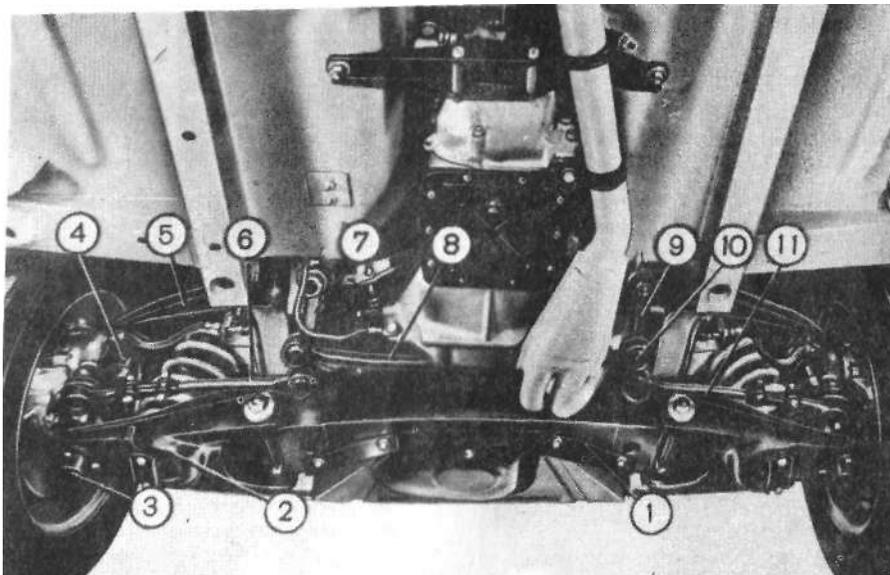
Передняя подвеска и рулевое управление: 1 — поперечина; 2 — нижний рычаг; 3 — шаровая опора нижнего рычага; 4 — шаровая опора верхнего рычага; 5 — верхний рычаг; 6 — боковая рулевая тяга левая; 7 — сошка; 8 — средняя рулевая тяга; 9 — маятниковый рычаг; 10 — шаровый шарнир; 11 — боковая рулевая тяга правая
